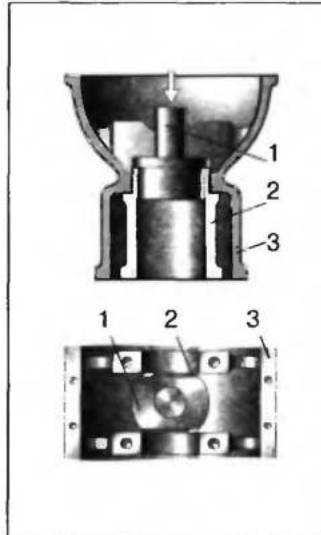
Оправка для выпрессовки "мокрых" гильз:
